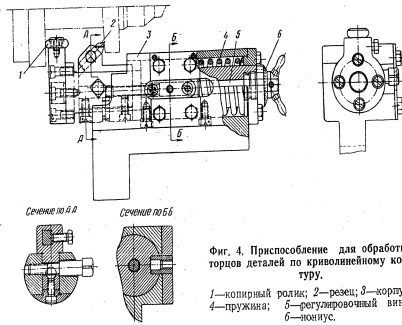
Приспособление для обработки торцов деталей по криволинейному контуру.
